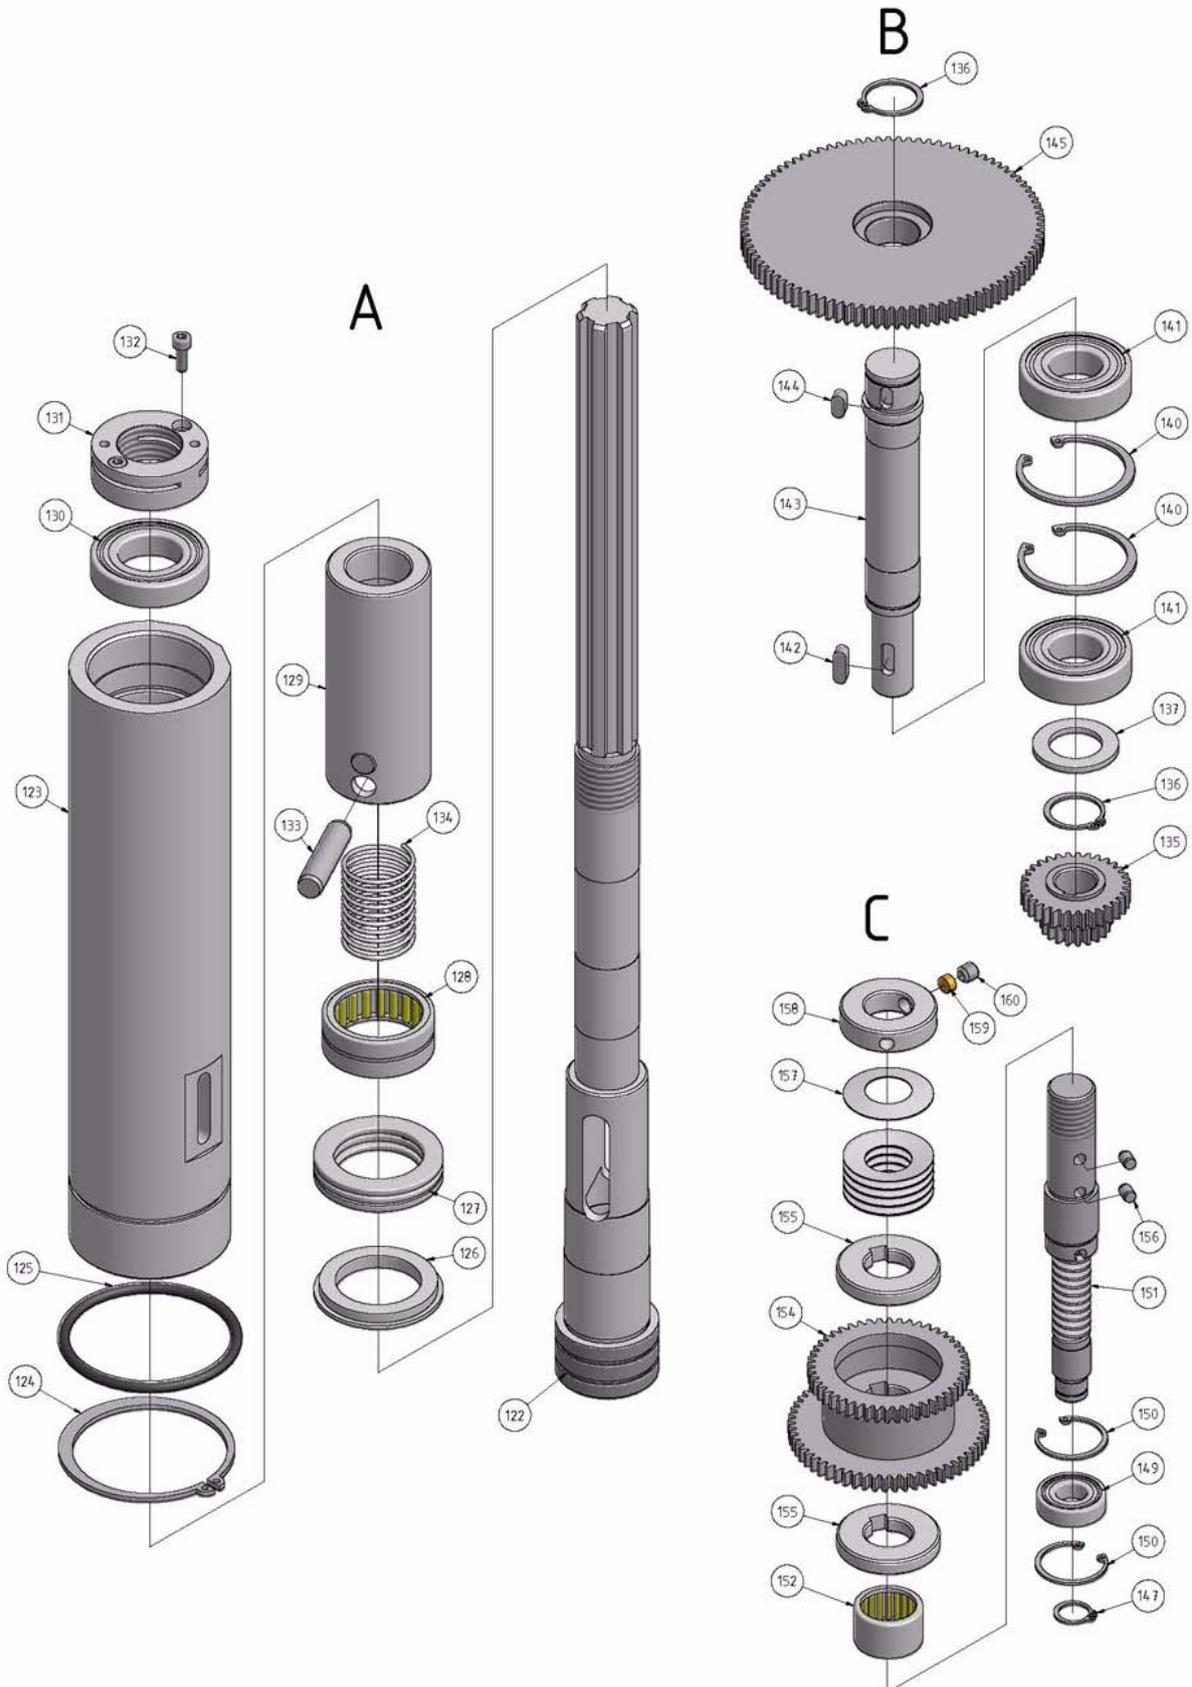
Vorschubgetriebe 1 von 4 - Feed gear box 1 of 4
